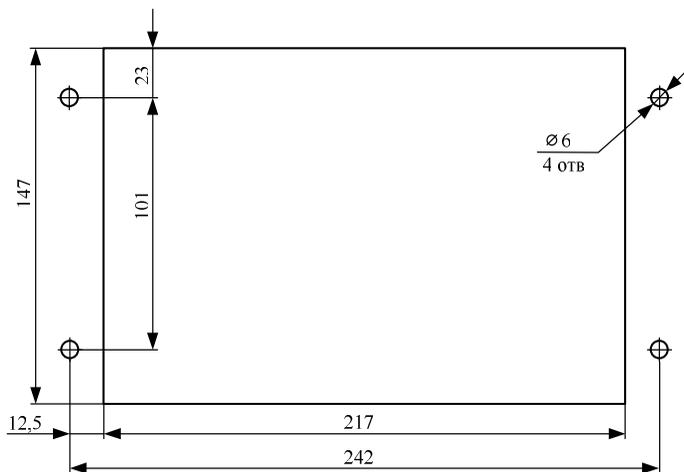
Размеры отверстий для установки преобразователя ТВ-011
